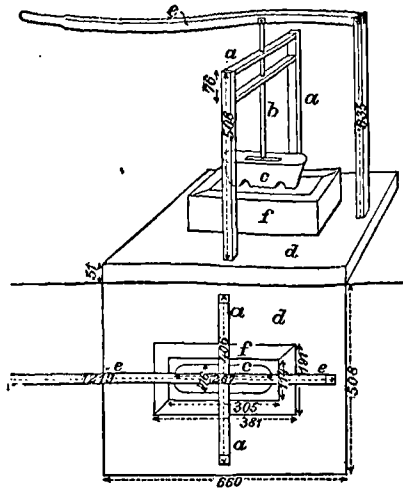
Presse pour la fabrication des moules en cuivre.
